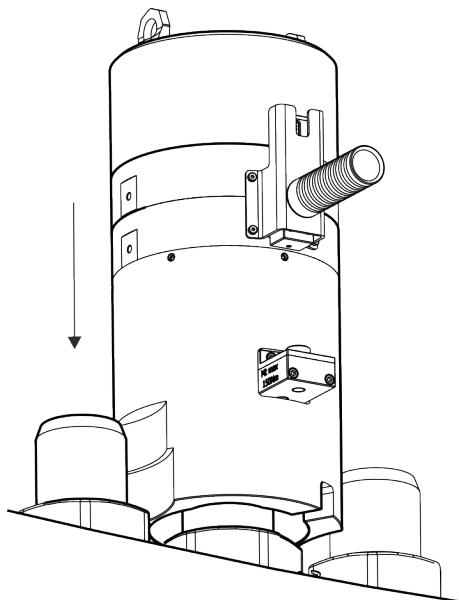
Spannzylinder auf Schraubverbindung setzen
